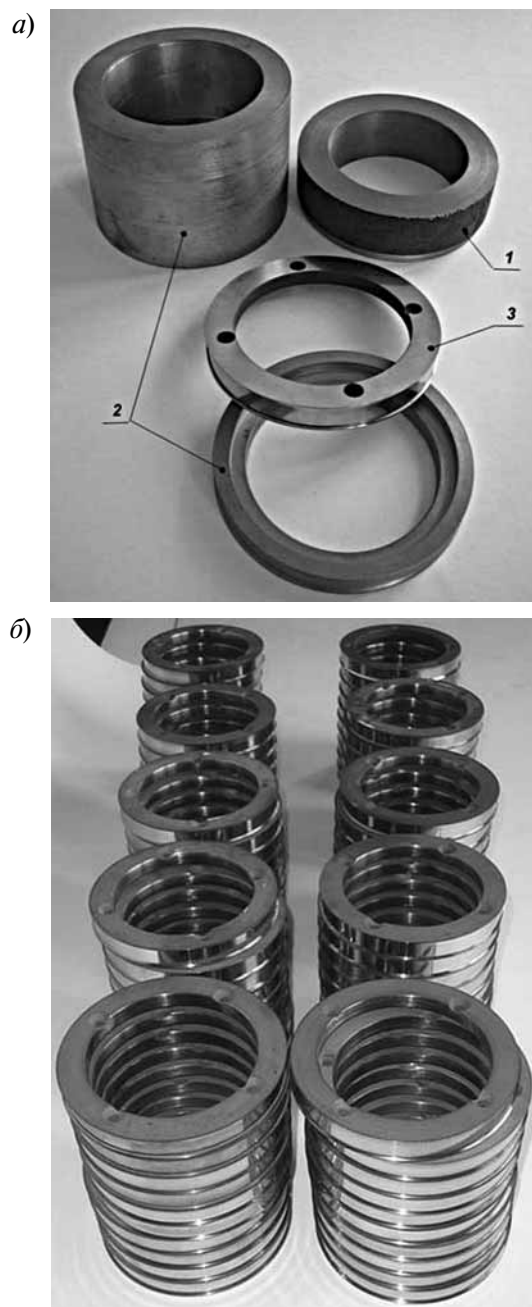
Обработанная отливка (1), заготовки (2) и деталь «диск тормозной» (3) из БВХЧ (а) и опытно-промышленная партия дисков тормозных (б)
